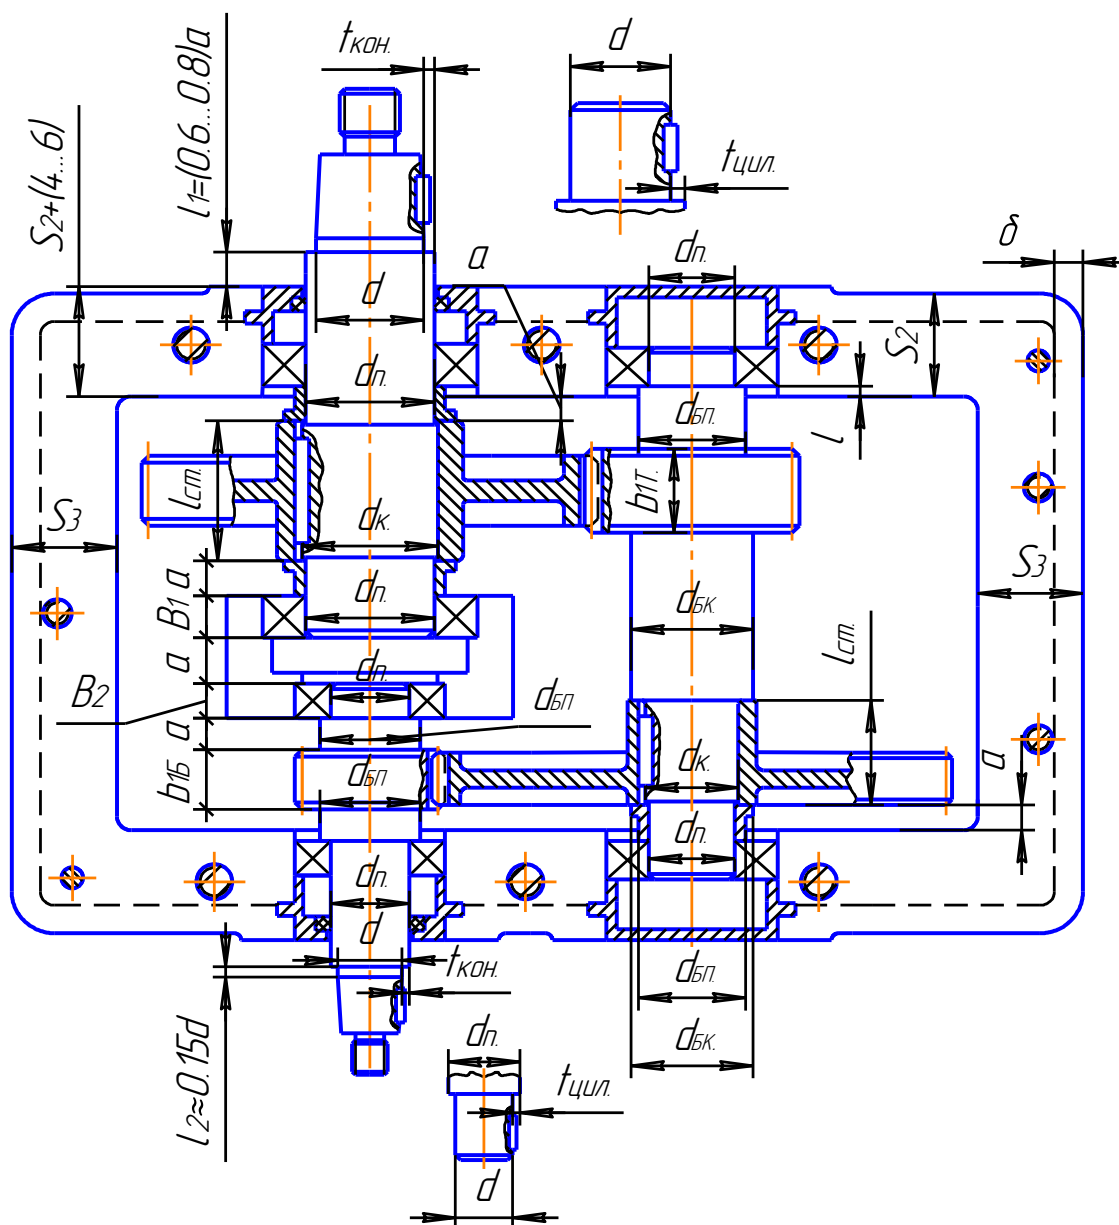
Компоновка цилиндрического двухступенчатого соосного редуктора с внутренним расположением подшипниковых бобышек
